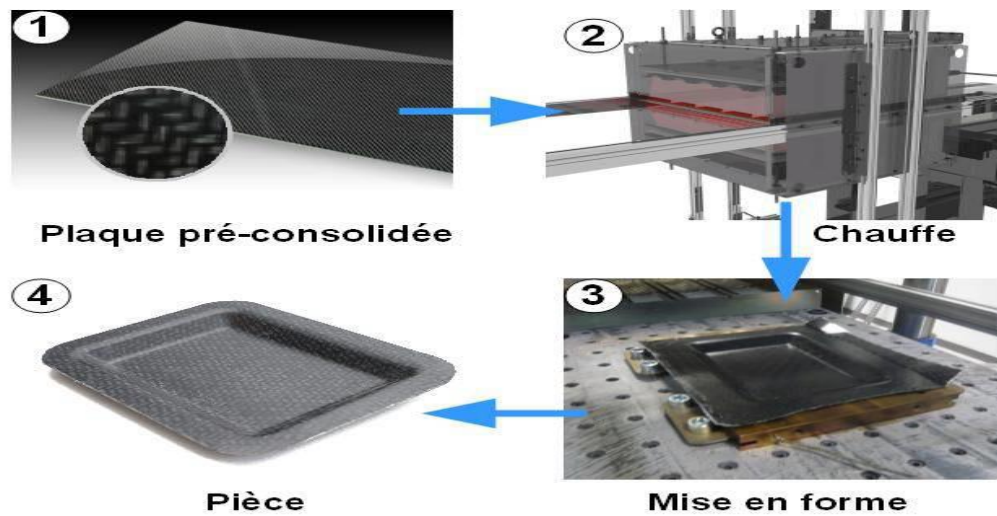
Schéma du procédé de thermo-estampage: 1) plaque pré-consolidée ; 2) chauffe dans le four ; 3) emboutissage du flan ; 4) pièce terminée [31].
